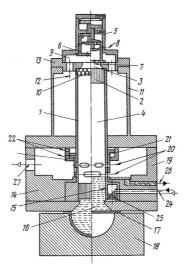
Схема импульсной пневматической машины для штамповки с цанговым зажимом бойка
